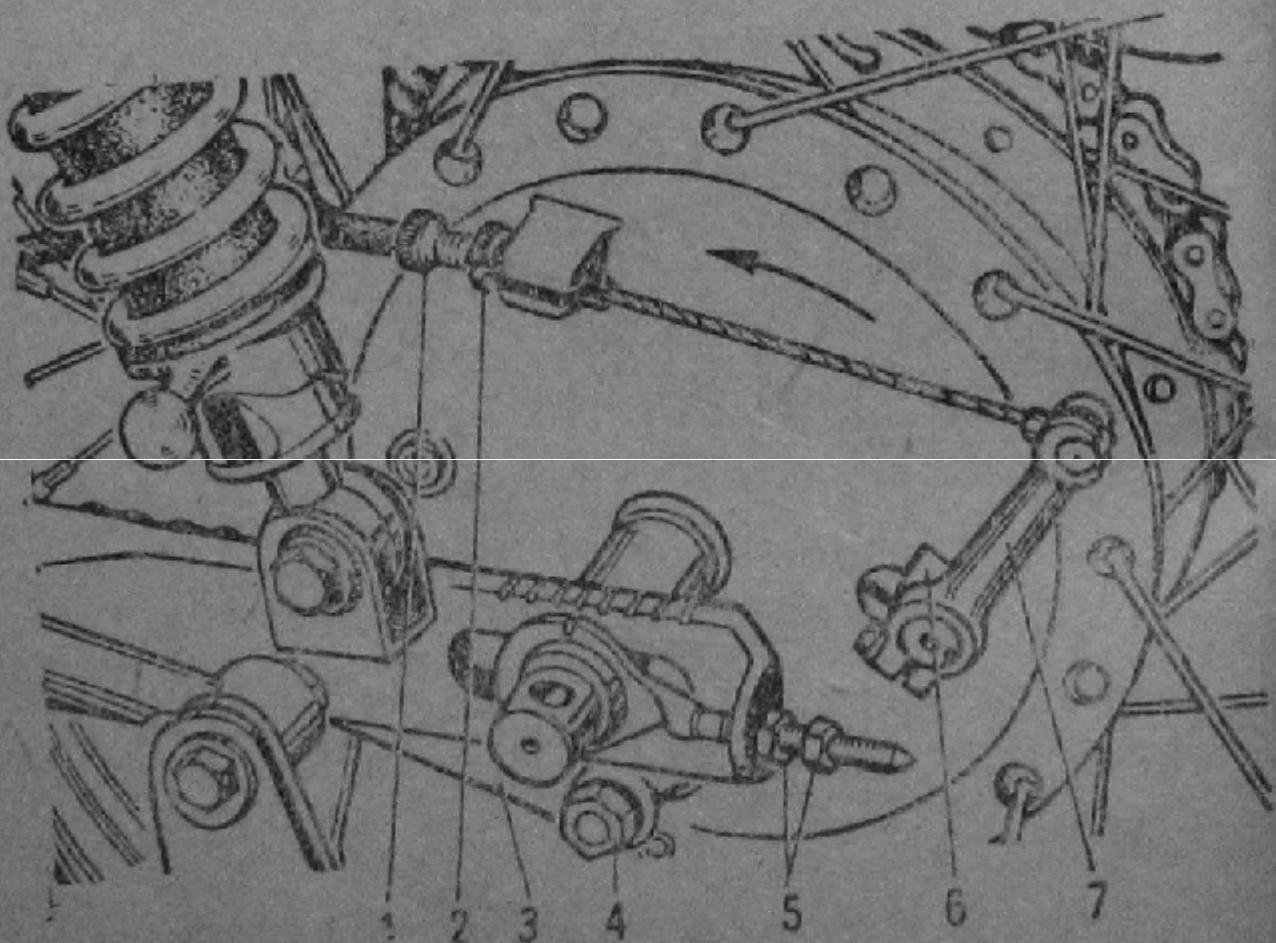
Снятие заднего колеса и регулировка тормоза заднего колеса:
